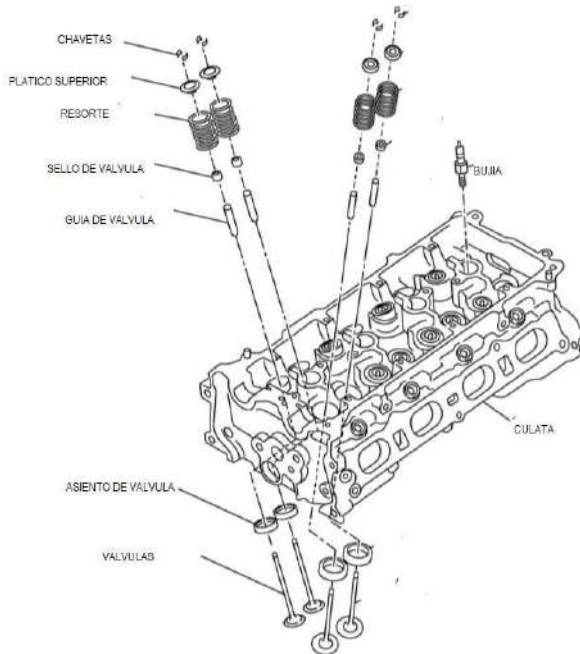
Componentes cabeza de cilindros. Nissan motor company.
